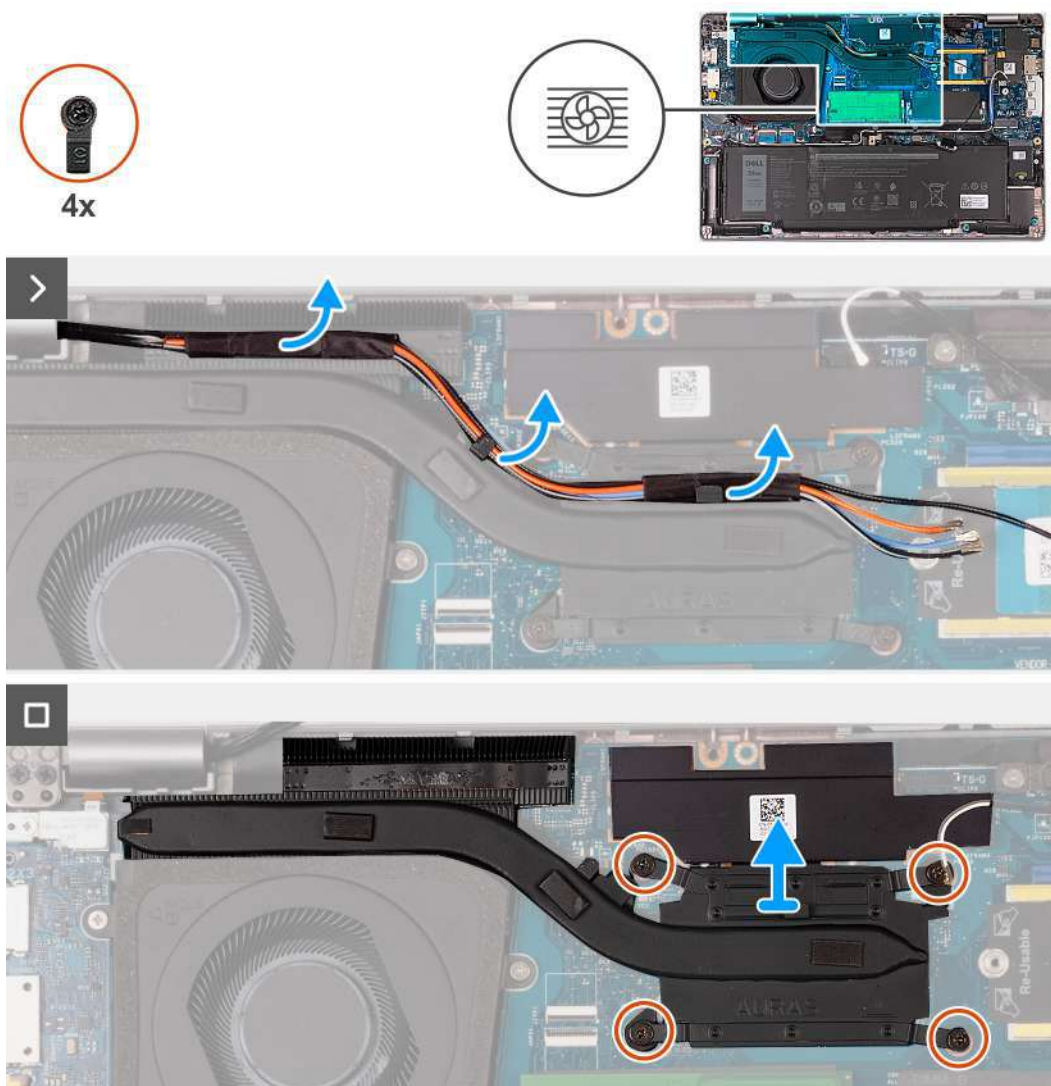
Como remover o dissipador de calor - computadores com placa 5G
